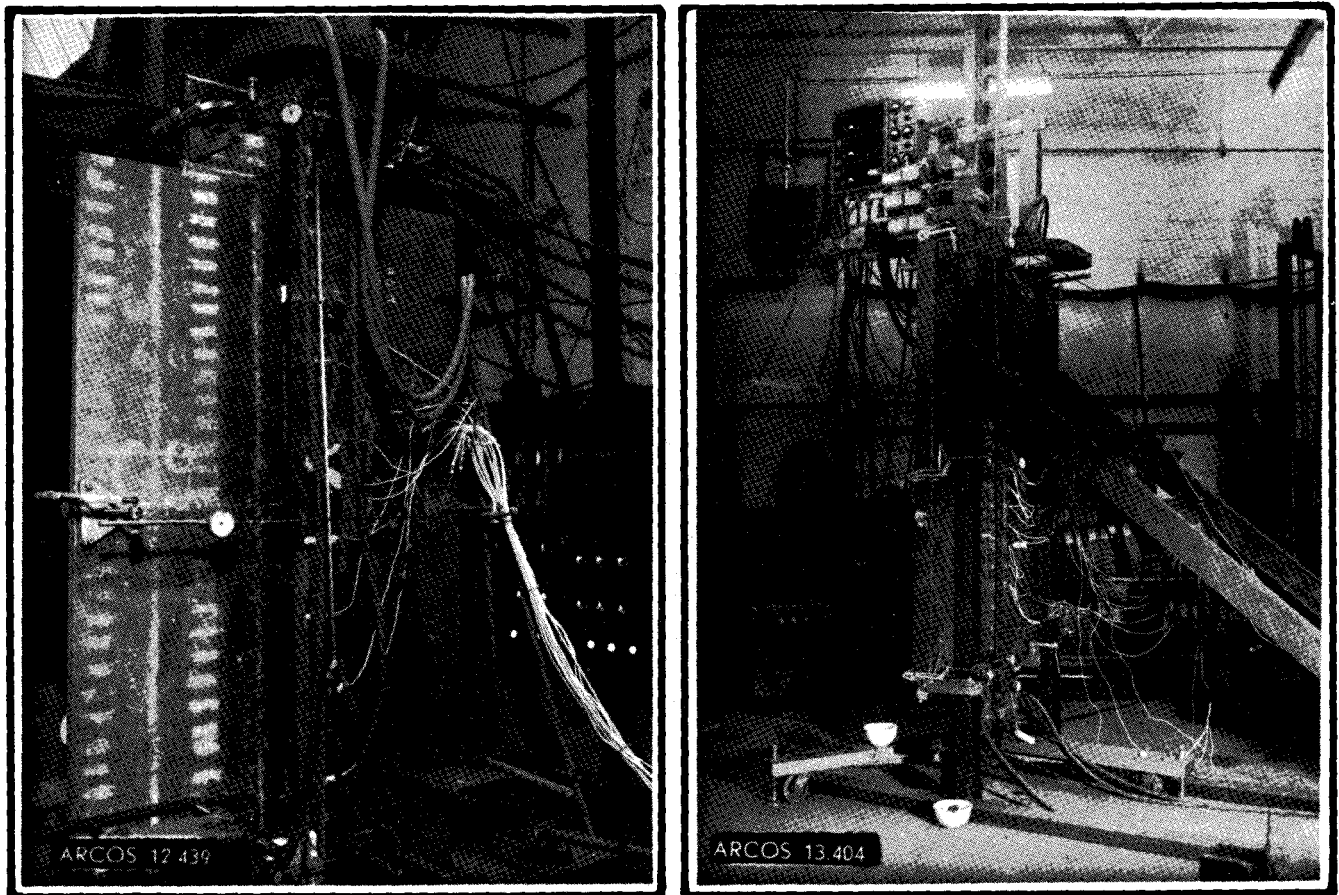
Éprouvettes en position de soudage
